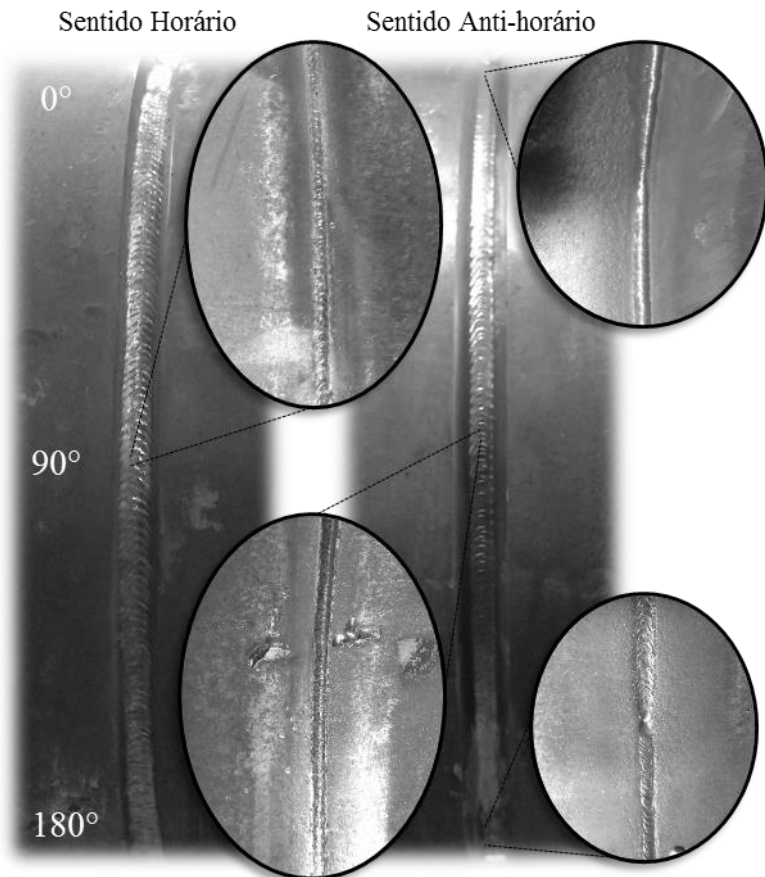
Corpo de prova 2 da matriz de ensaios com solda.
